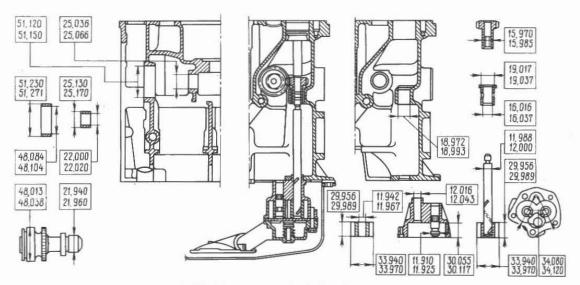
Dimensiones principales de la bomba de aceite y de su mando
